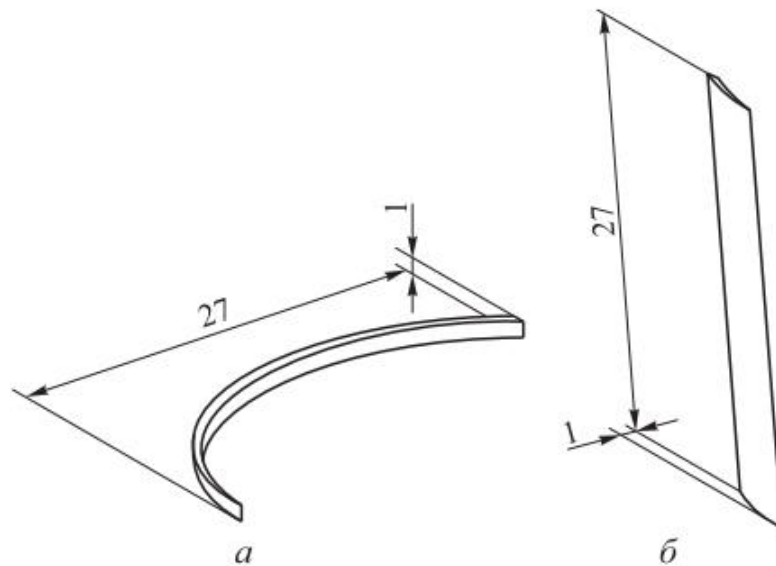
Форма стружки однакового об'єму для торцювого (а) і циліндричного (б) фрезерування
